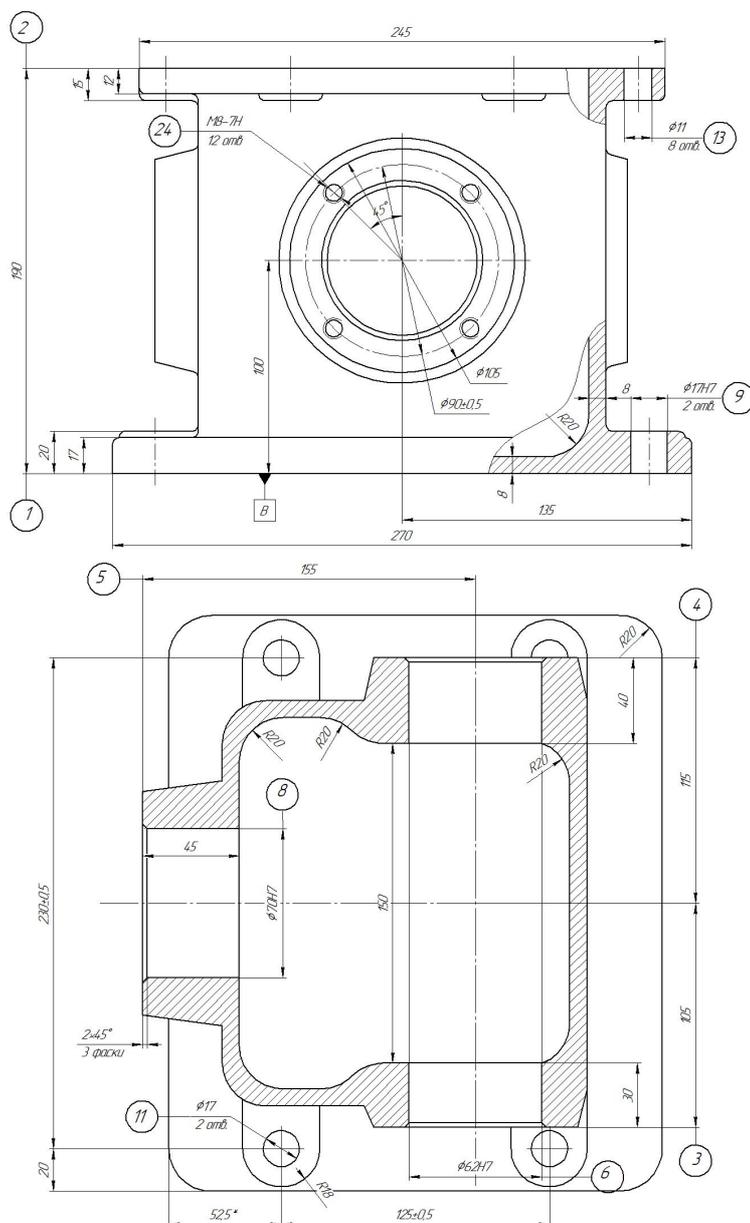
Эскиз детали с номерами обрабатываемых поверхностей
